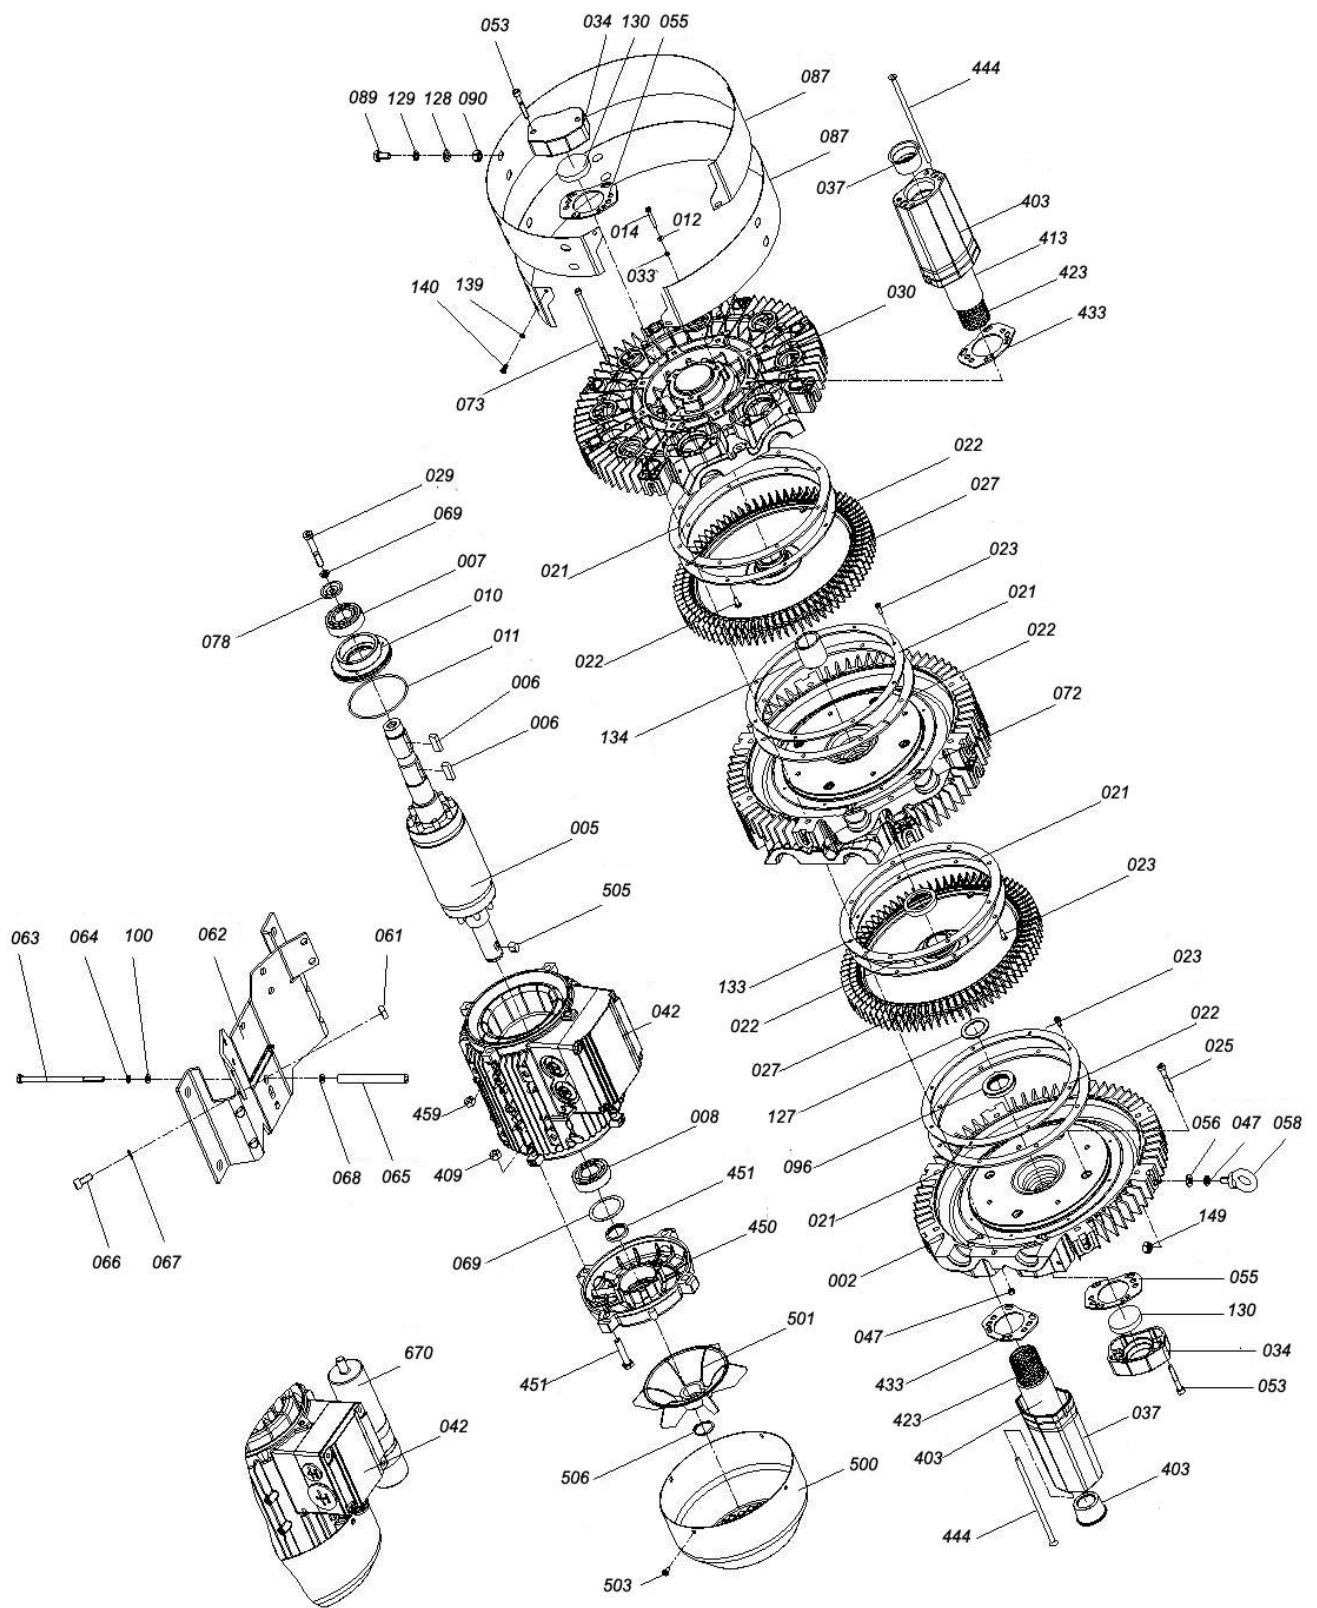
Деталировка двухступенчатых воздуходувок 4RB
